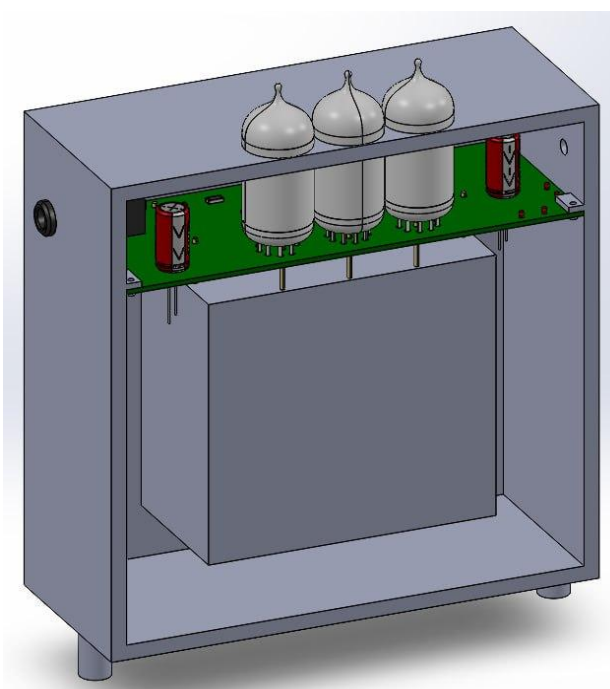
Частина корпусу з платою гітарного підсилювача
